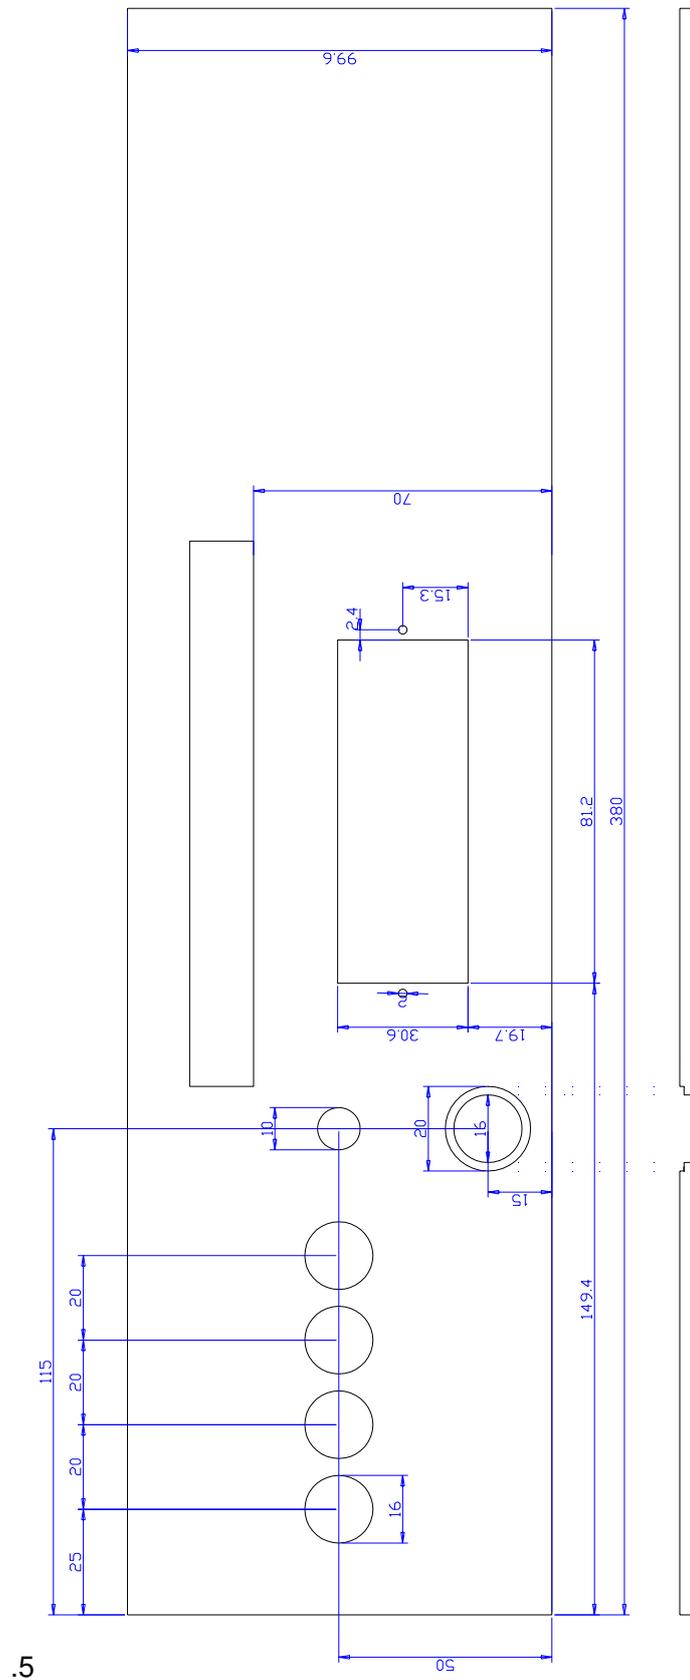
Technische Zeichnung der Blende M 1:2
